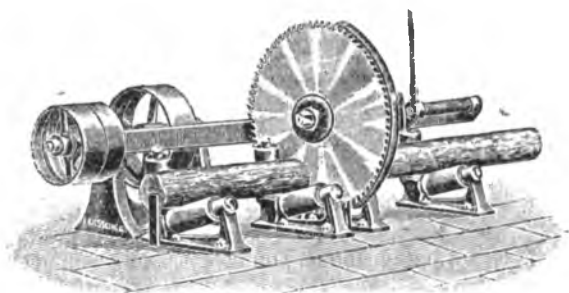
Станок с круглой пилой для поперечной распиловки бревен.
